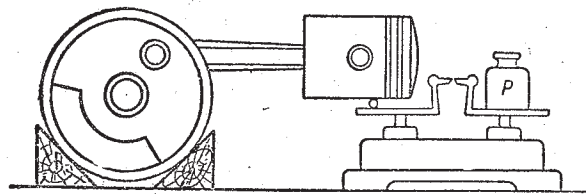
Способ взвешивания поршня и верхней части шатуна в сборе
